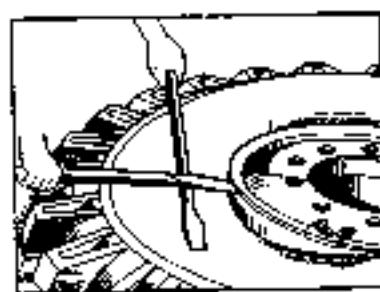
Einlegen des Reifenwulstes in die Montagerille der Felge
